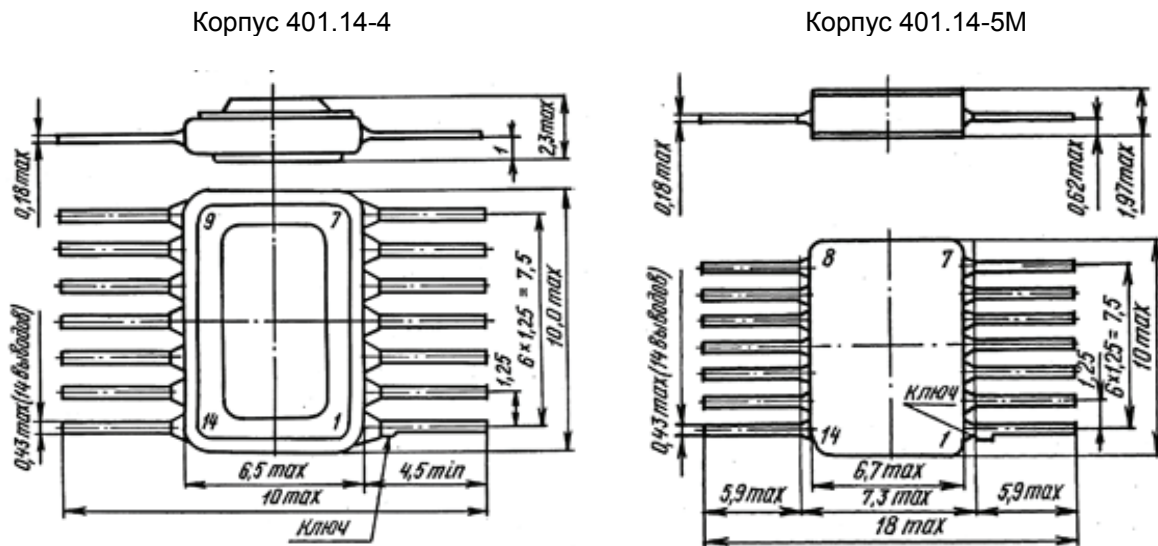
Габаритные чертежи корпусов 401.14-4 и 401.14-5M
